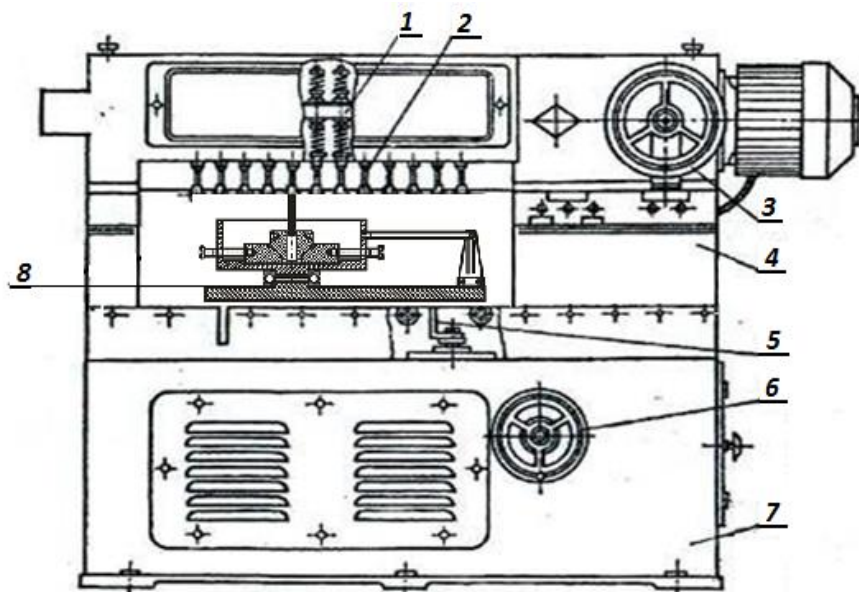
Лабораторна установка для дослідження працездатності абразивного складу: 1 – блок шпинделів; 2 – перехідник; 3, 6 – маховик; 4 – стійка права; 5 – косинець підйомного столу; 7 – станина; 8 – робочий вузол для притирання
